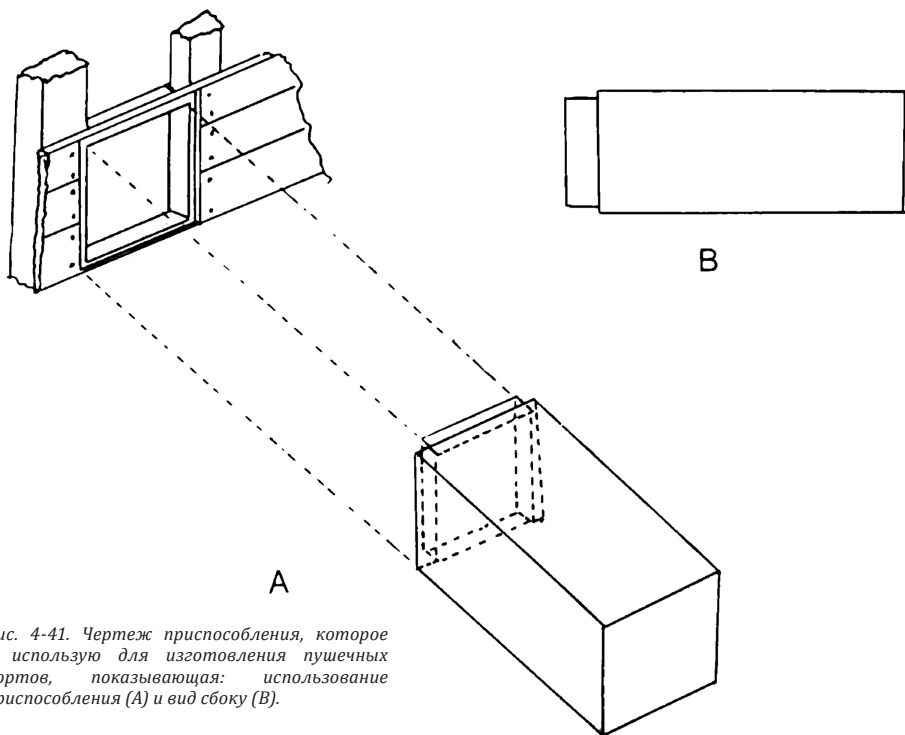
Чертеж приспособления, которое я использую для изготовления пушечных портов, показывающая: использование приспособления (А) и вид сбоку (В).
